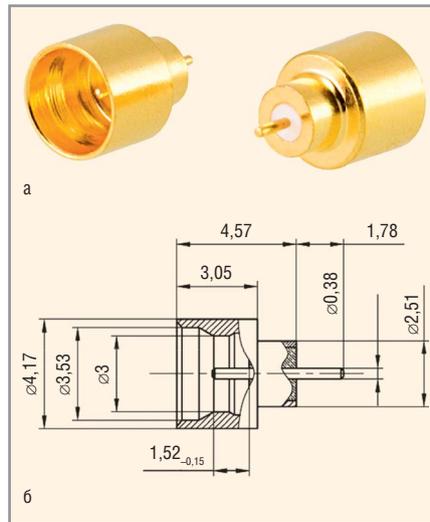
Соединитель SMP-ВБМГП-Х-1-327-1.С:
